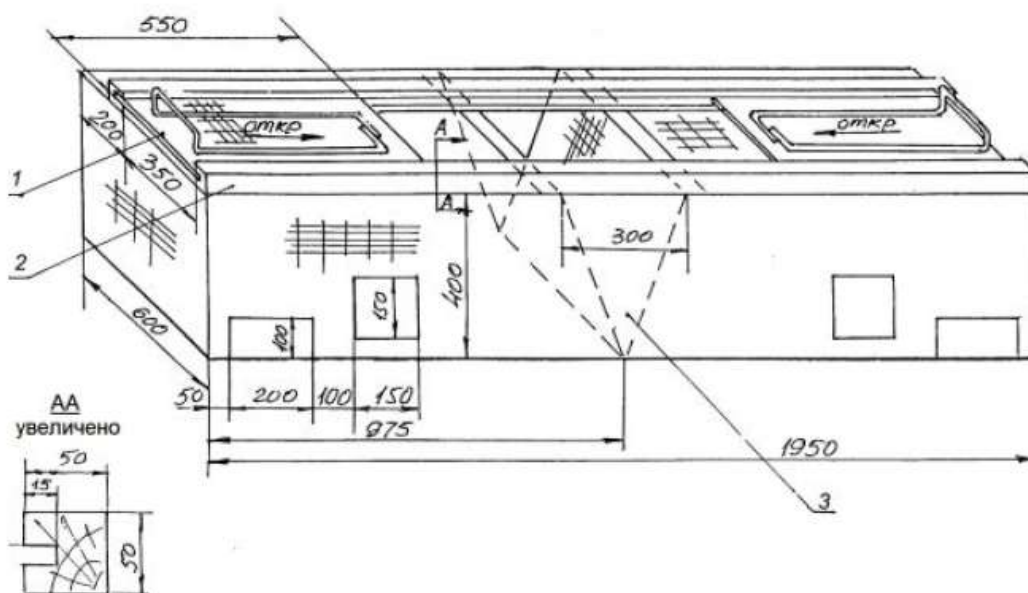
Двухклеточный блок нижнего яруса: 1 – выдвигающаяся дверка; 2 – направляющий брусок дверок; 3 – ясли для грубых кормов
